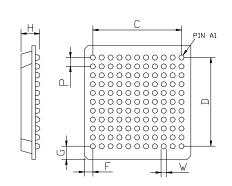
1.0mm PBGA 元件焊盘的标准尺寸
